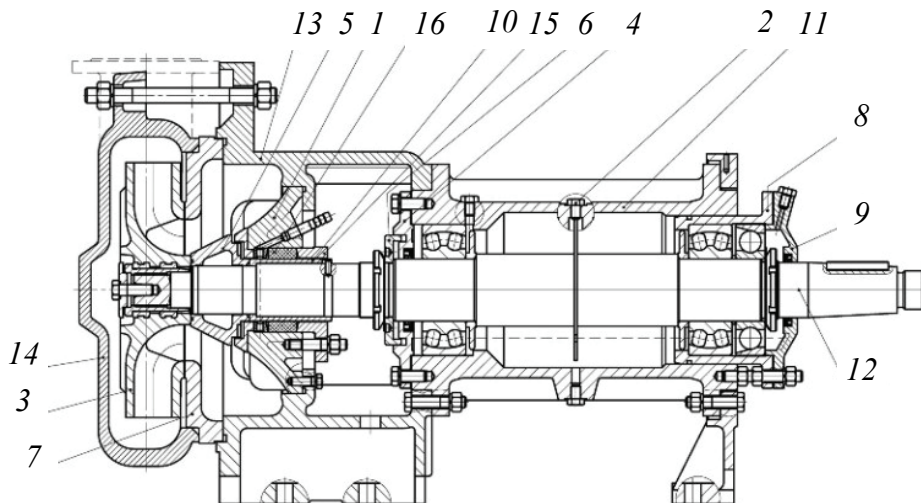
Общий вид песковых насосов типа 1 ПБА: 1 – корпус сальника; 2 – маслоуказатель; 3 – колесо рабочее; 4 – крышка прижимная; 5 – импеллер; 6 – крышка лабиринта; 7 – диск; 8 – гильза; 9 – крышка прижимная; 10 – втулка сальника; 11 – стакан; 12 – вал; 13 – корпус подвода; 14 – отвод; 15 – крышка сальника; 16 – сальник вала
